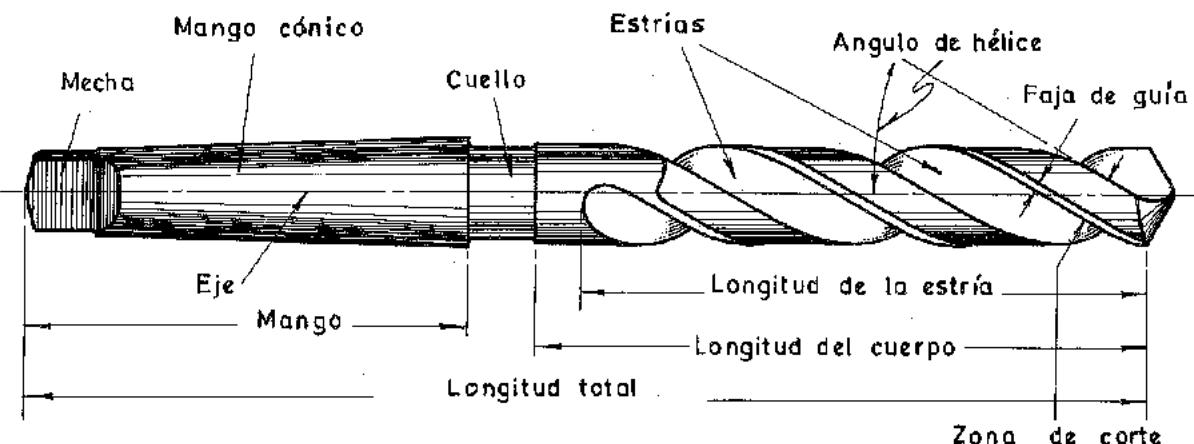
Partes principales de una broca helicoidal (Morse Twist Drill & Machine Co.).
